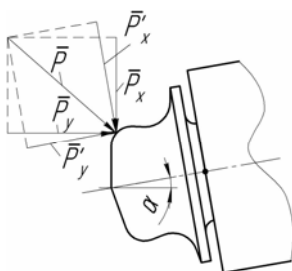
Розкладання повного зусилля, що діє на валок вздовж осі обертання валка та вздовж осі обертання заготовки
